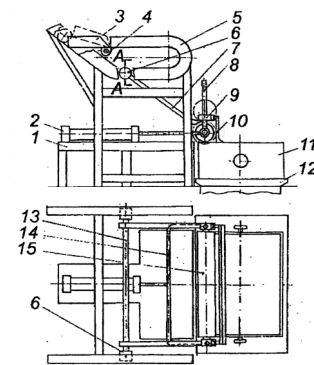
Устройство для удаления излишка формовочной смеси с опоки:
